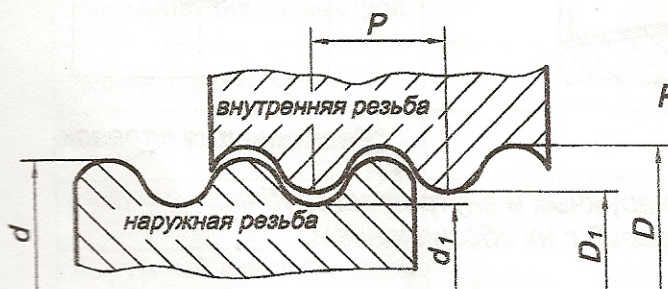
Профиль и основные параметры резьбы Эдиссона круглой:
